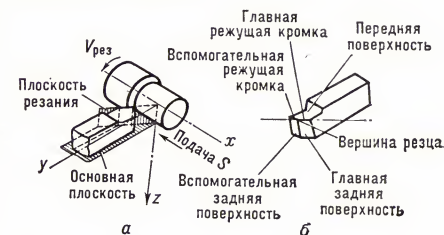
Схема процесса резания (а) и основные элементы резца (б).
